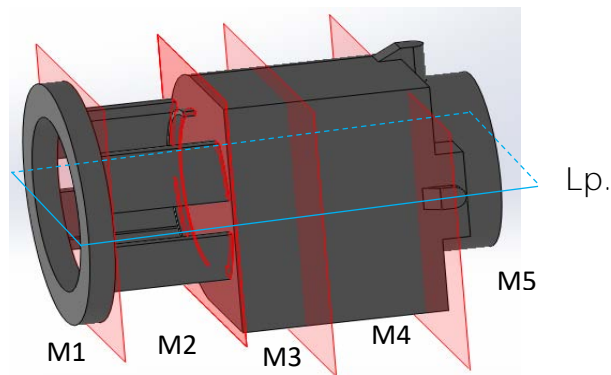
Dibujo 3D de la pieza problema, indicando la posición de la línea de partición (LP).
